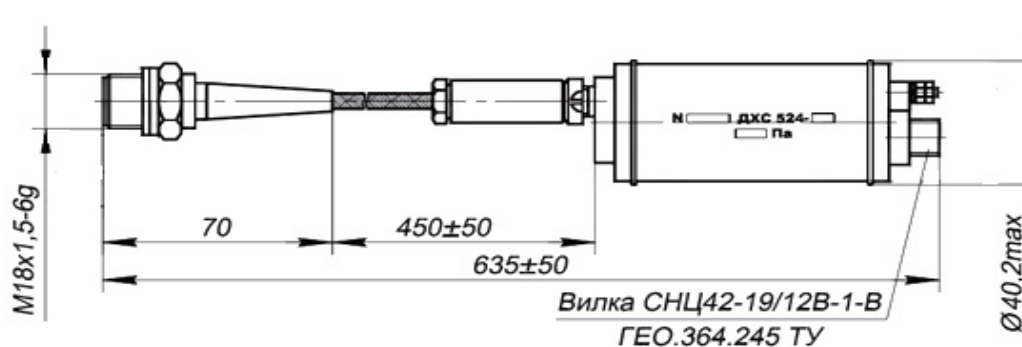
Габаритные и установочные размеры датчика ДХС 524
